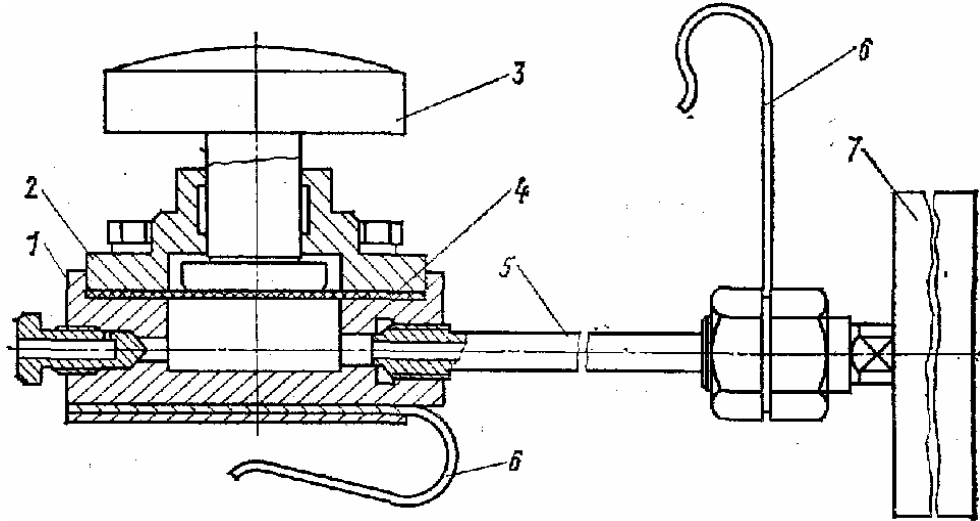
Силвимірювальний пристрій стенда К-208М:
